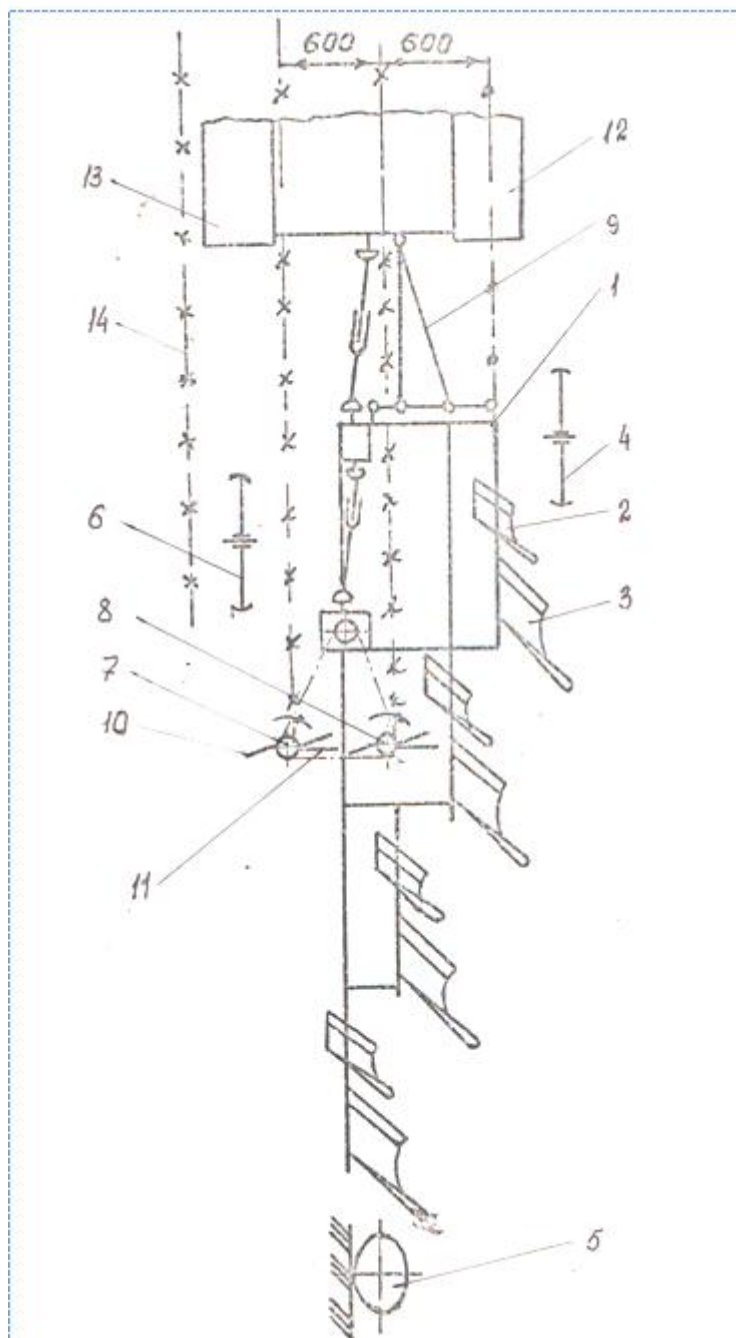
Конструктивно - технологическая схема комбинированного двухъярусного плуга ПЯ-4-30 (вид сверху).
